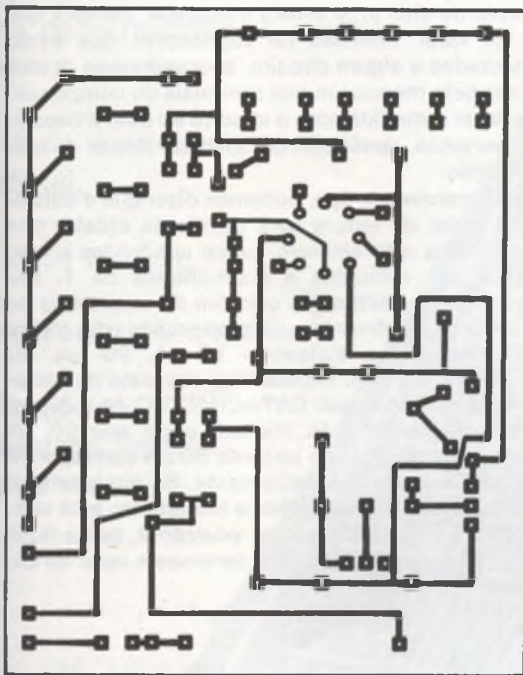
A- Placa de Circuito Impresso vista pelo lado cobreado.
